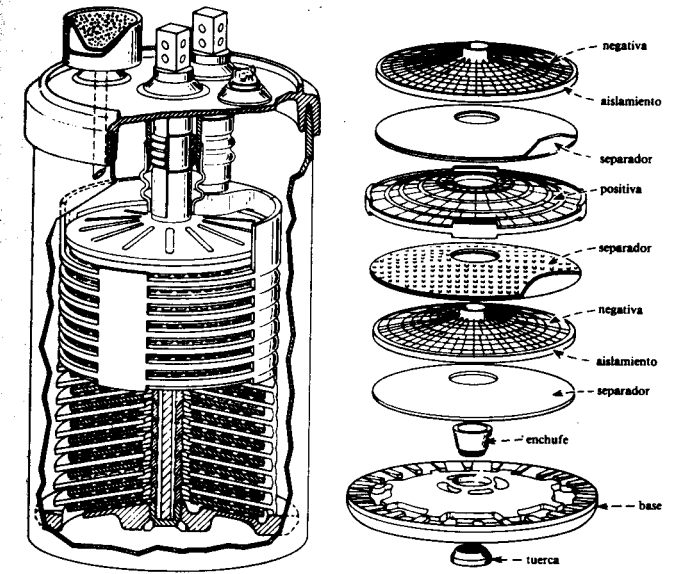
La batería del sistema Bell (corte y vista de las piezas).
